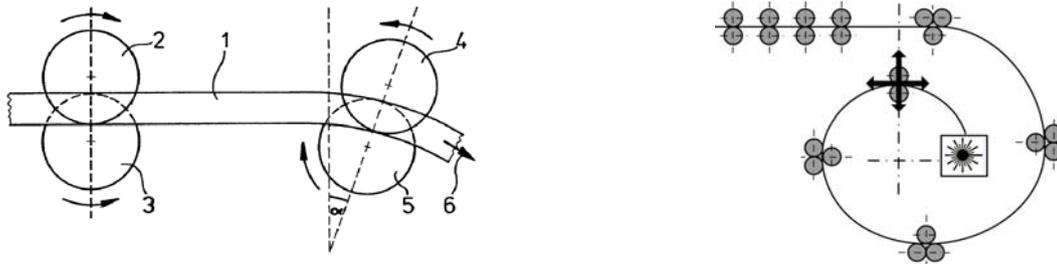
Verfahrensprinzip zum Biegen unter Zugkraftüberlagerung nach KIRSCHNING [103] (rechts)
